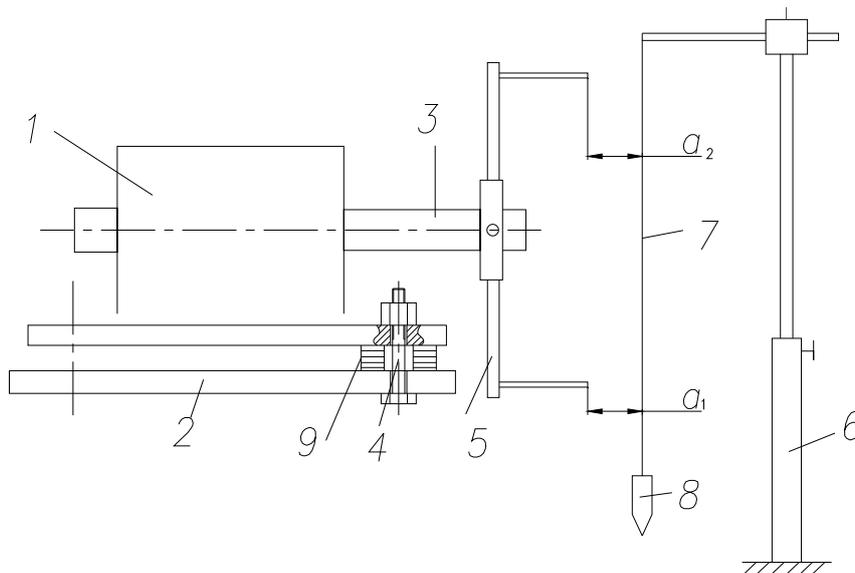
Схема опытной установки для проверки горизонтальности вала
